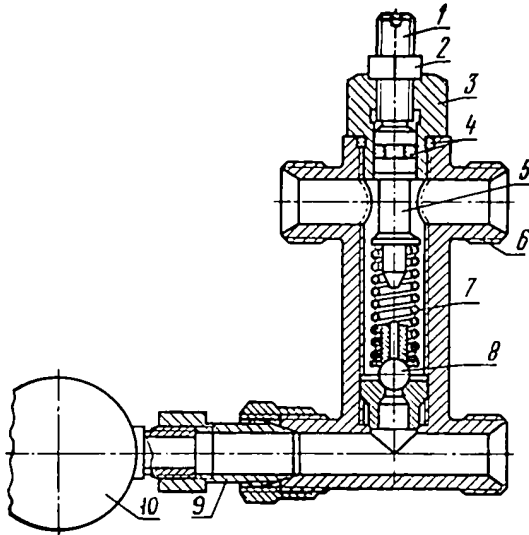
Предохранительный клапан: 3 - гайка; 4- уплотнительное кольцо; 5 - шток; 6 - корпус; 7 - пружина; 8 - шарик; 9 - переходник
